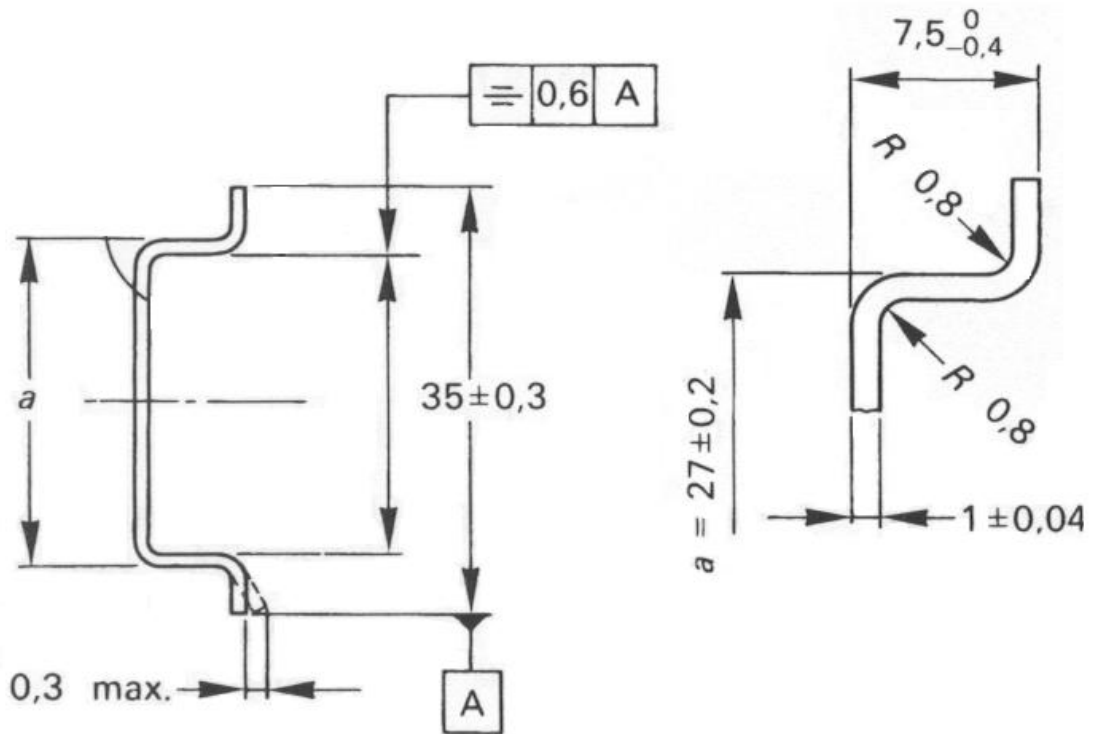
Dimensões (mm) das calhas metálicas de perfil normalizado do tipo TH 35-7.5
